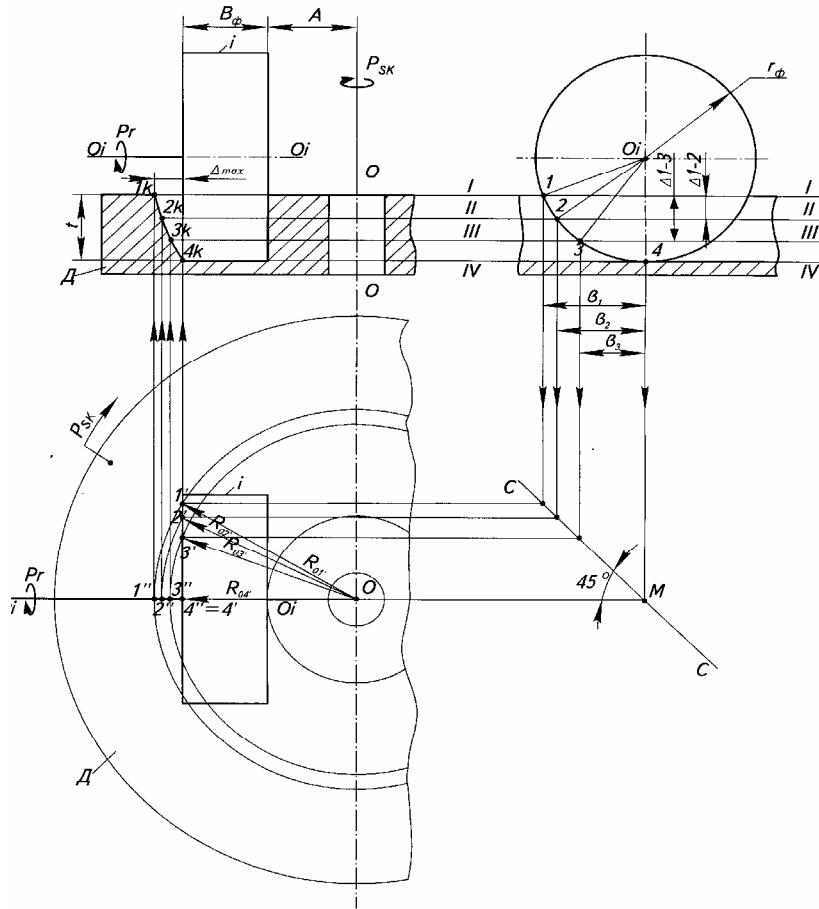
Схема обробки для випадку перетину вісей обертання дискової фрези і деталі
